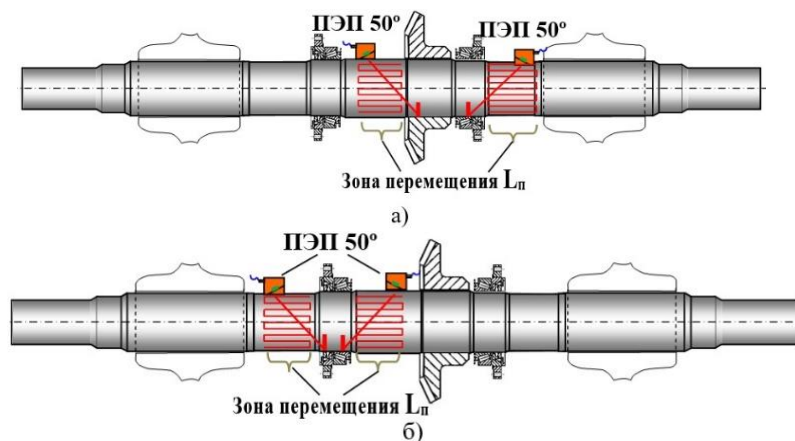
Контроль участка оси под зубчатым колесом и редукторным подшипником (а) и участка оси под отдельно напрессованным редукторным подшипником (б) вариантом метода AR 3.2
